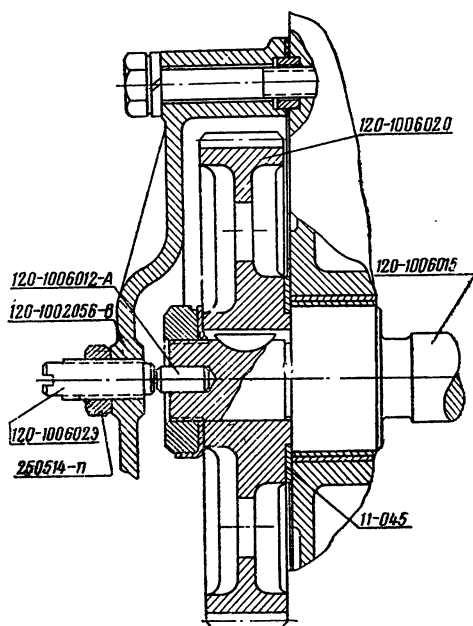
Установка распределительного вала с помощью регулировочного винта двигателя ЗИЛ-124
